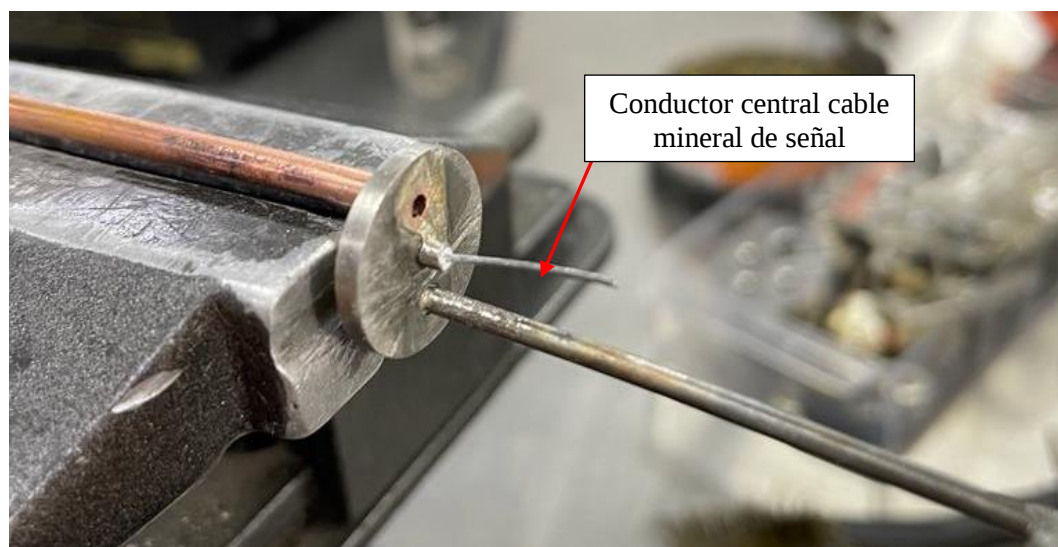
Tapa soldada con cables minerales y tubo de cobre.
